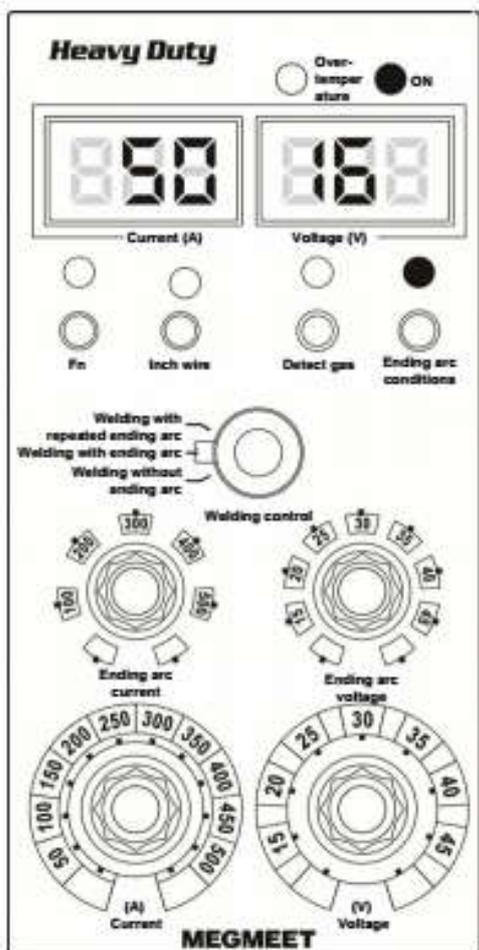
Выбор сварки с режимом заварки кратера
